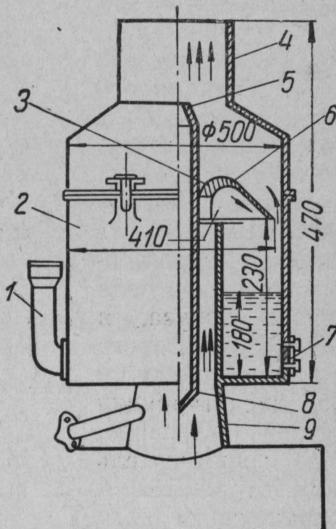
Искрогаситель с орошением для локомобиля П-25;
